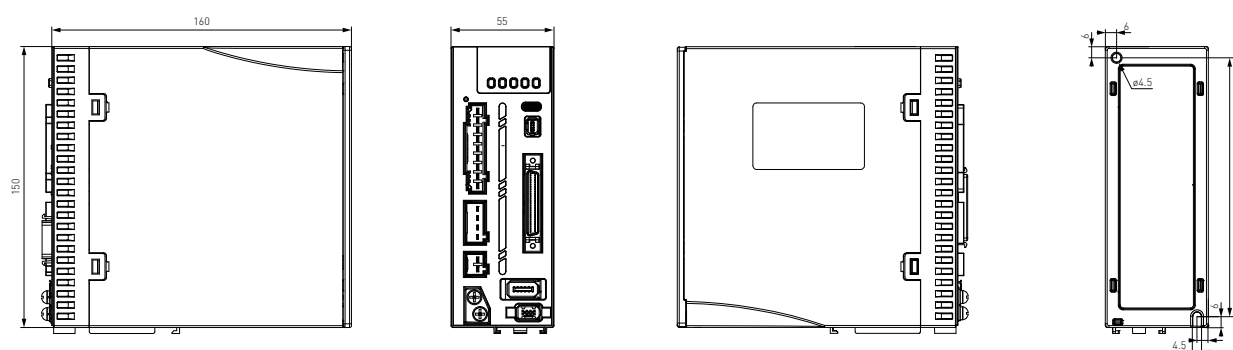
Габаритные размеры драйверов EL8-RS750F и EL8-RS1000F.
